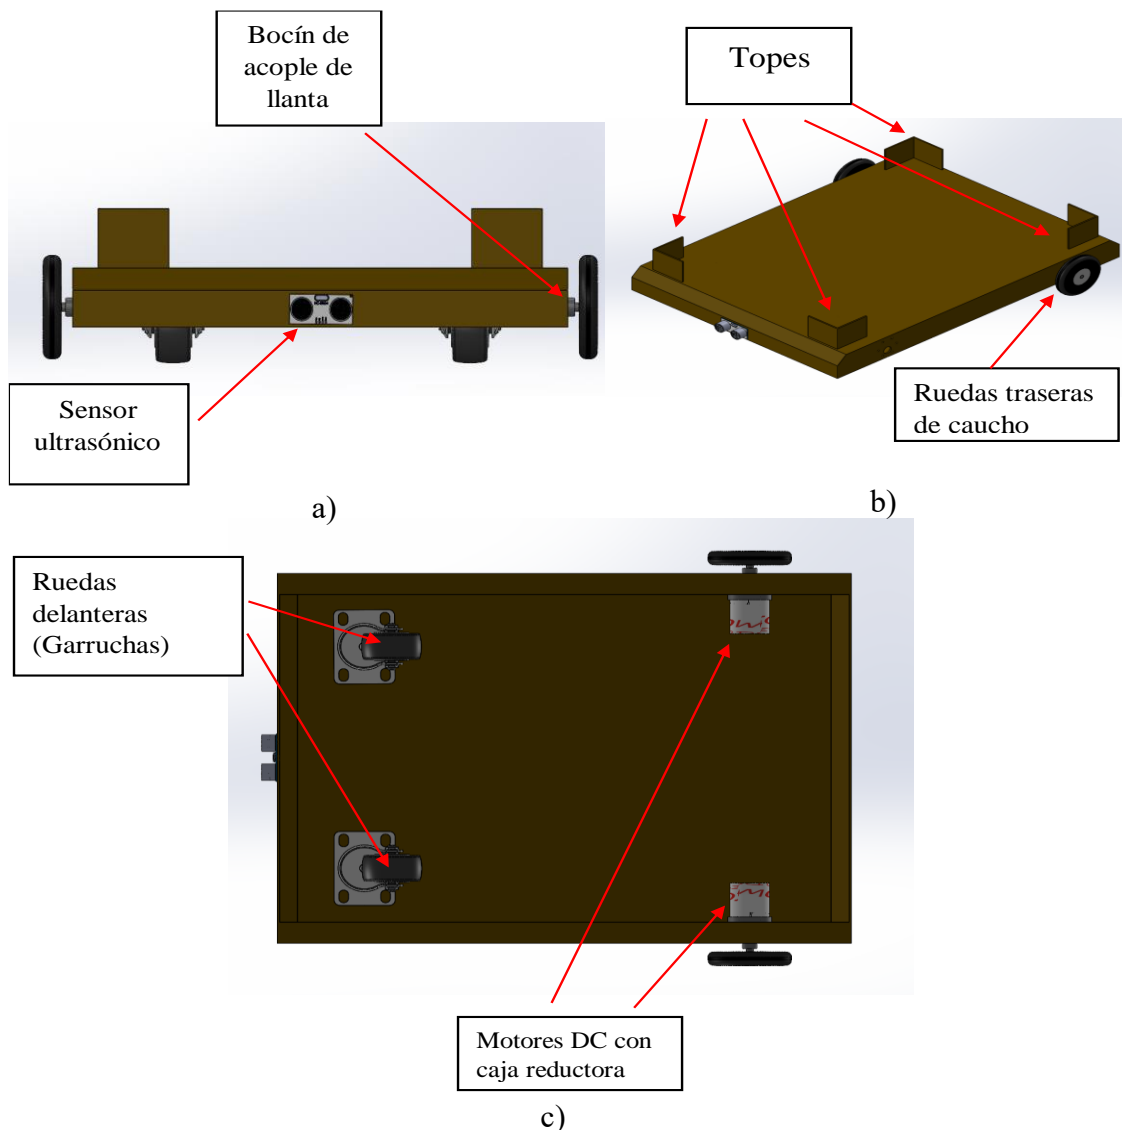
a) Vista frontal, b) Vista isométrica frontal izquierda, c) Vista inferior
